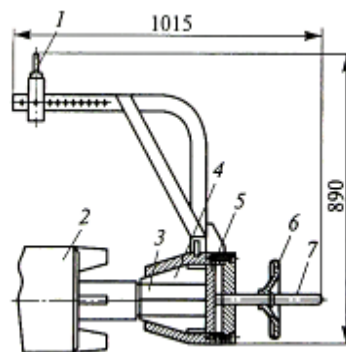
Пристрій для виймання та закладення ротора: 1 – серезжки; 2 – ротор; 3 – вал; 4 – кулачки; 5 – пластина; 6 – рукоятка; 7 – вісь
